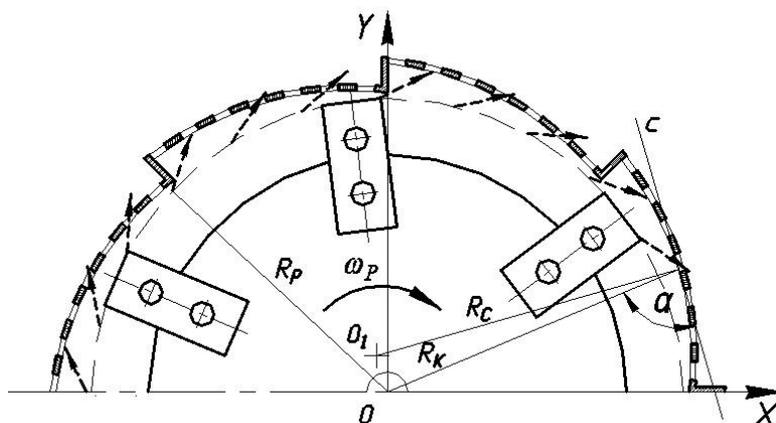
Схема к определению геометрических параметров сегментного решета дробильной камеры
